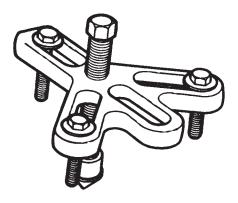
Ferramenta de Remoção do Abafador de Vibração 7697
